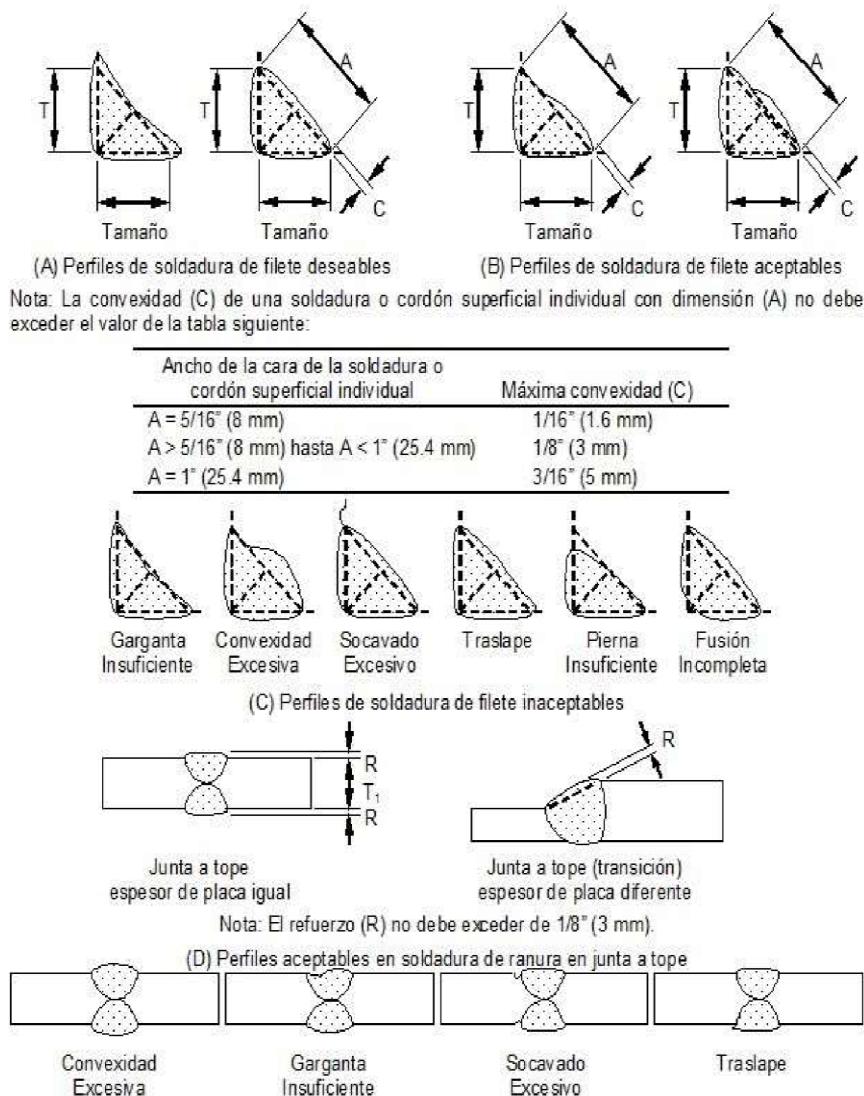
Perfiles inaceptables en soldadura de ranura en junta a tope.
